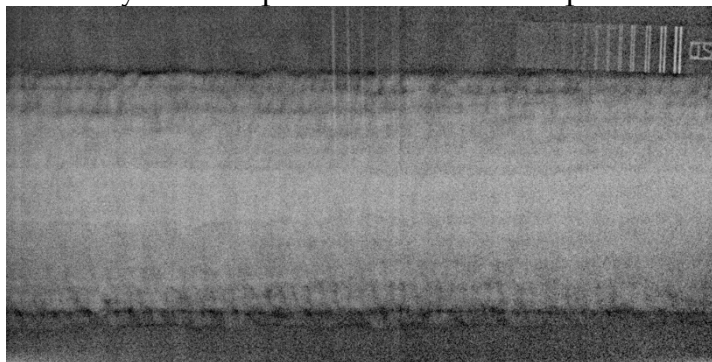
Сварное соединений толстостенной корпусной конструкции
